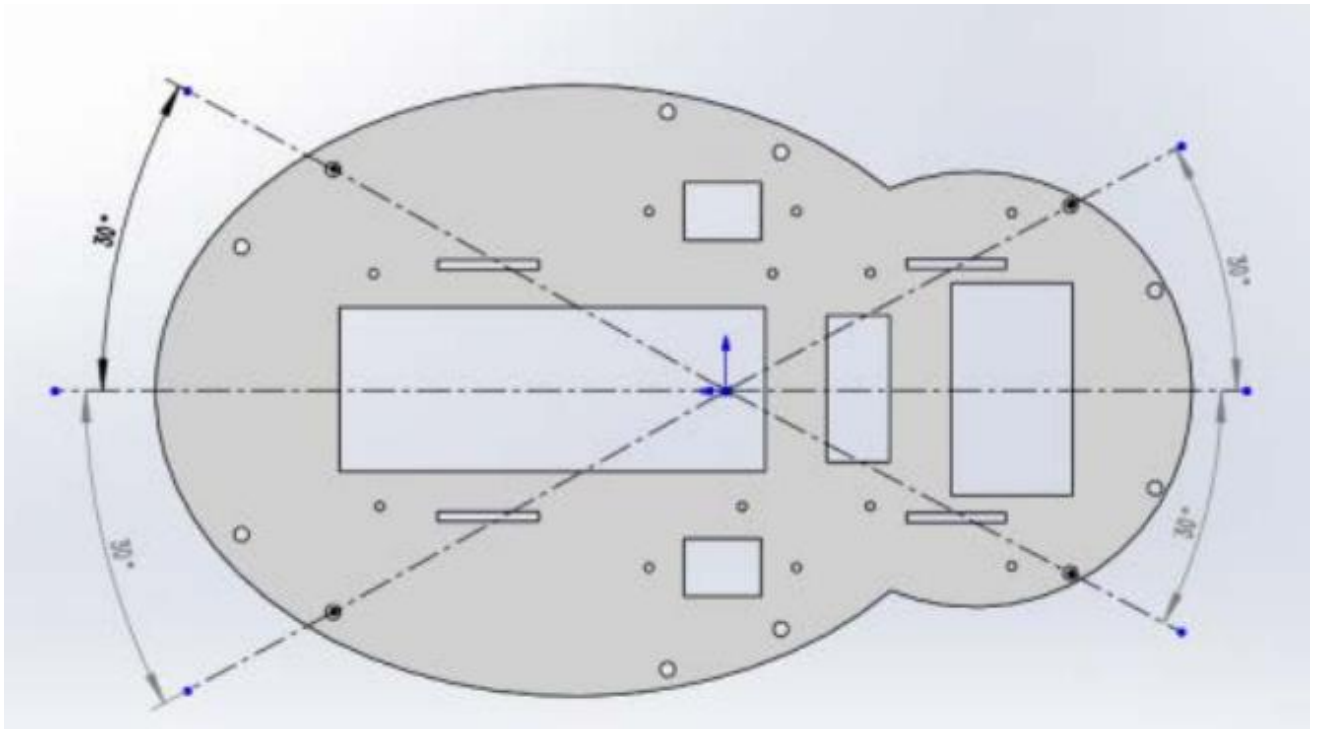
Загальний вигляд основи для корпусу МРТ
